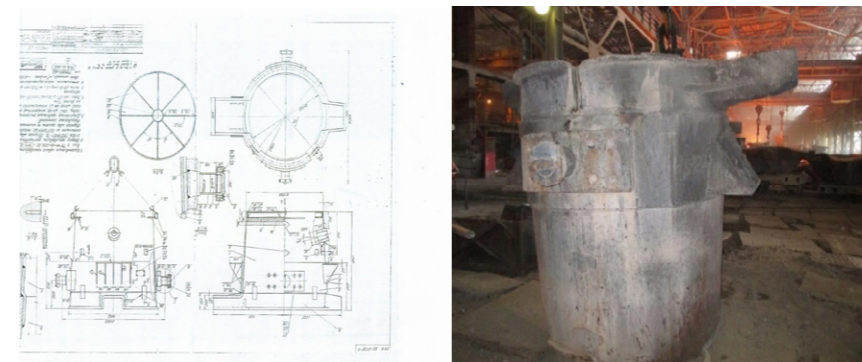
Сборочный чертеж и общий вид разливочного ковша ПЦ-1
